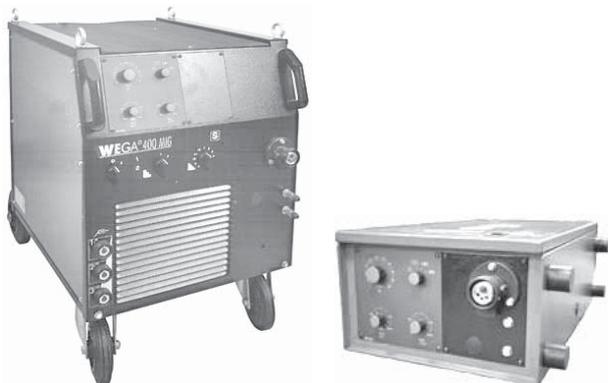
Наплавочное оборудование: сварочный полуавтомат ВЕГА-МИГ-400
